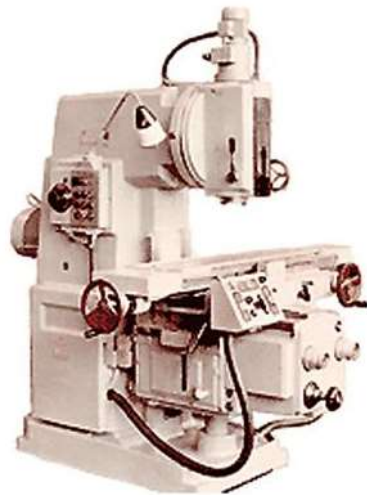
Вертикально-фрезерний станок 6P11
